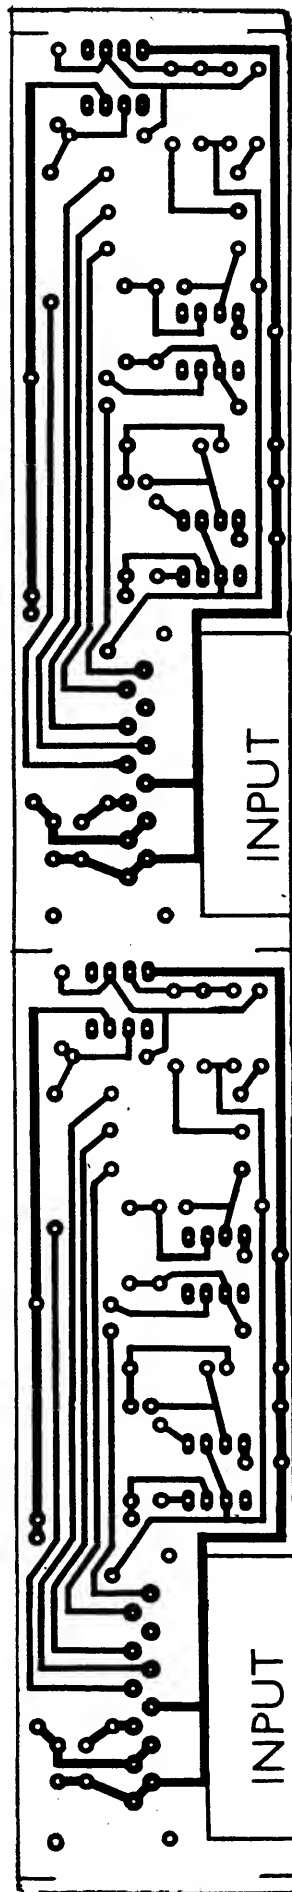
Deska Y305 s plošnými spoji DPX 223 – základní deska
